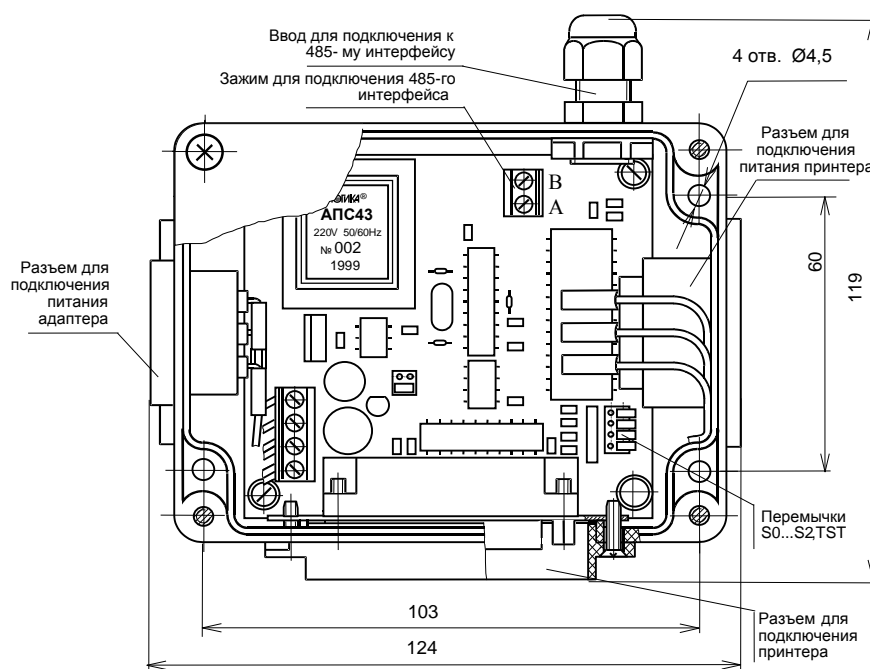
Присоединительные размеры корпуса адаптера АПС43
